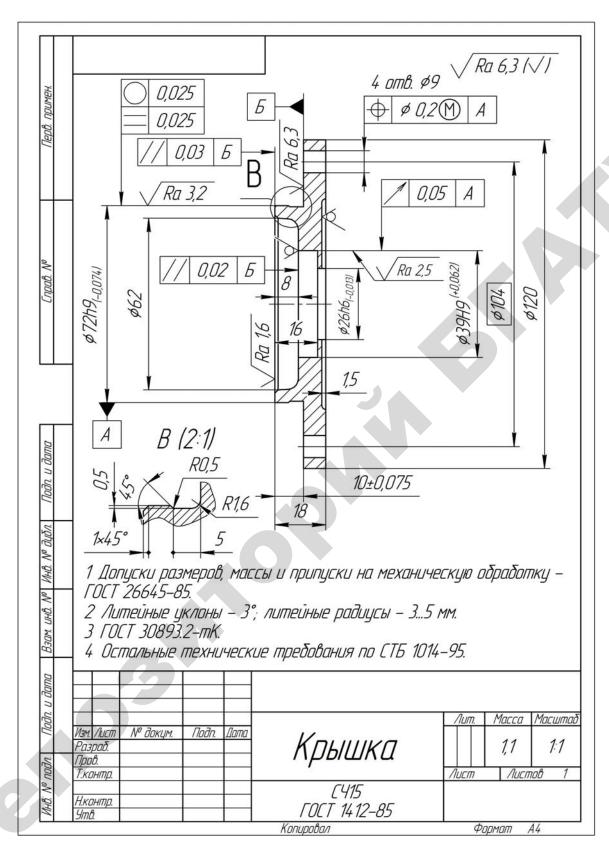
Пример выполнения чертежа сквозной крышки подшипника
